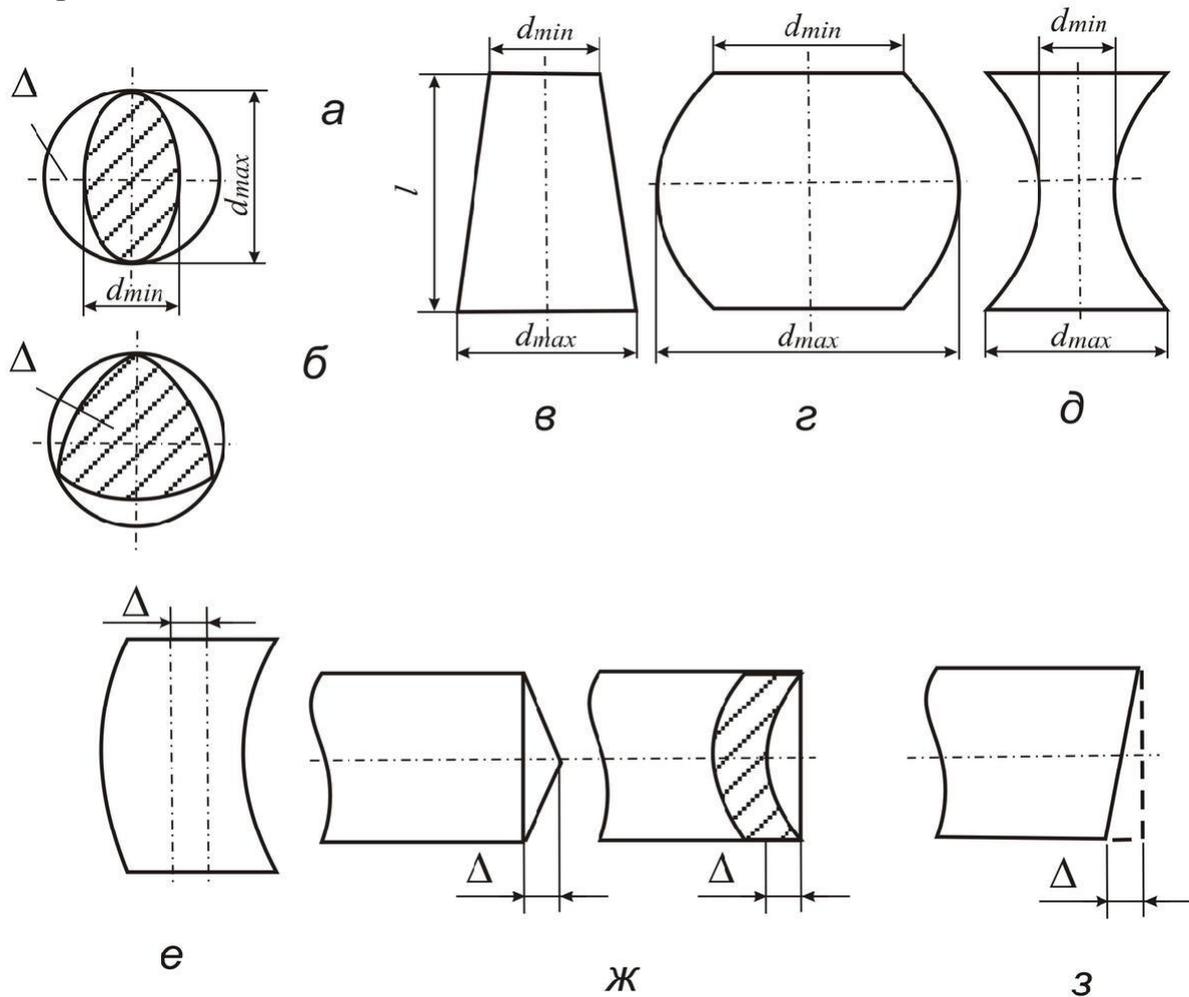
Основные виды дефектов цилиндрических и торцевых поверхностей
